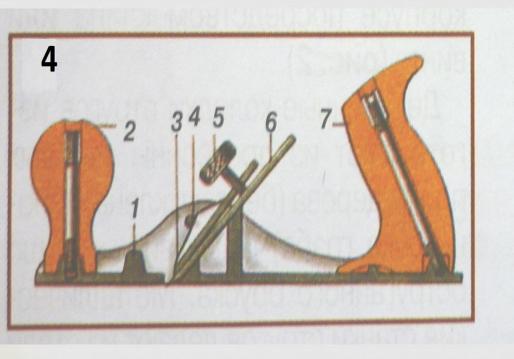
Одинарный металлический рубанок: 1— корпус; 2— рукоятка (передняя ручка); 3— прижим; 4— упорный стержень; 5— прижимный винт; 6— нож; 7— ручка (задняя).
